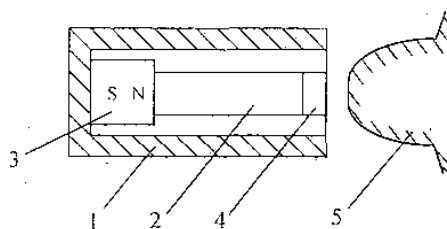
Упрощенная конструкция ДЧВ с цилиндрической магнитной системой: 1 - внешний магнитопровод; 2 - внутренний магнитопровод; 3 - постоянный магнит; 4 - преобразователь Холла; 5 - зубчатое колесо
